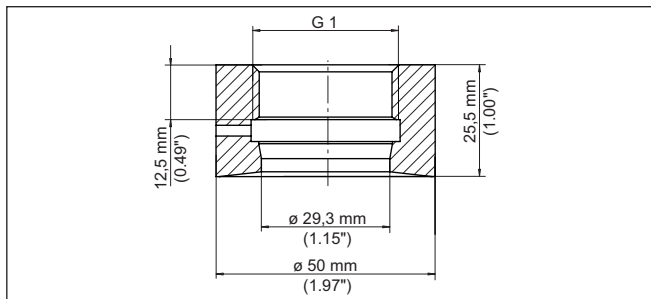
Dimensions raccord à souder direct G1 (ISO 228-1) - joint torique
